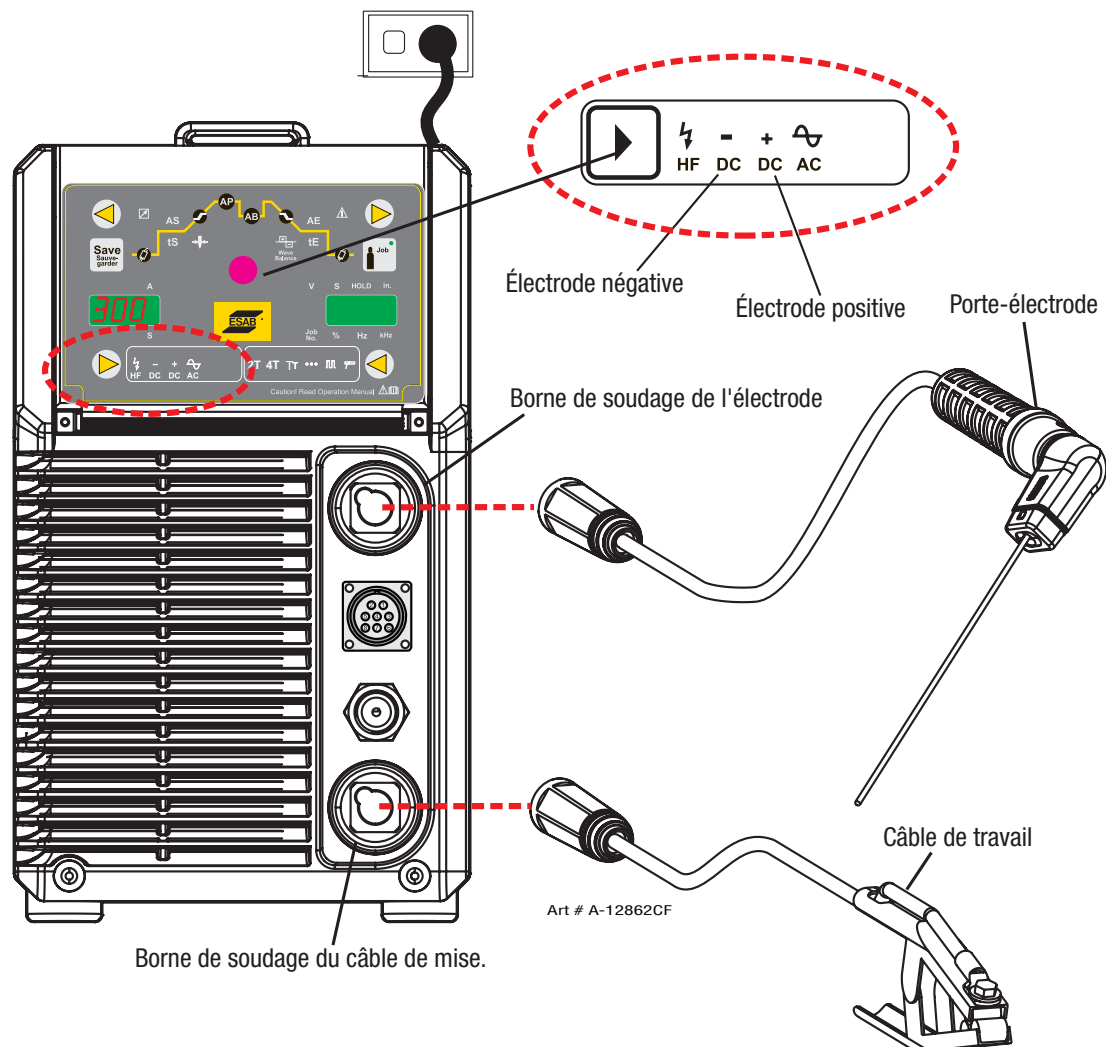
configuration pour soudage manuel à l'arc.
